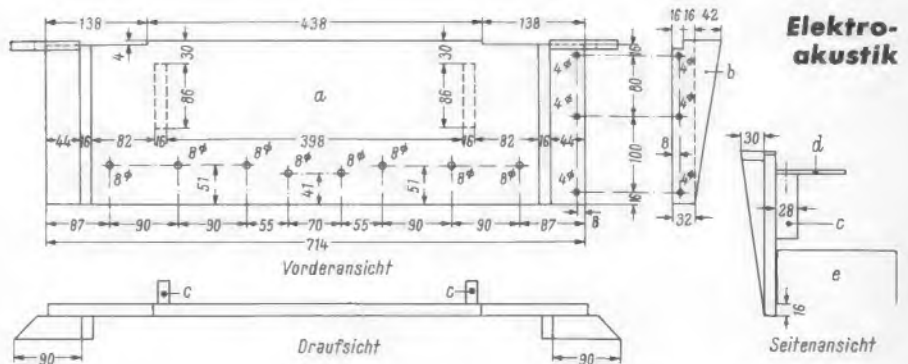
Die Frontplatte wird aus einer 16-mm-Tischlerplatte angefertigt. Es bedeuten: a = Raum für die Skala, b = Profilblech rechts und links, c = Stützen für die obere Bedienungsplatte, d = e = Hauptchassis
